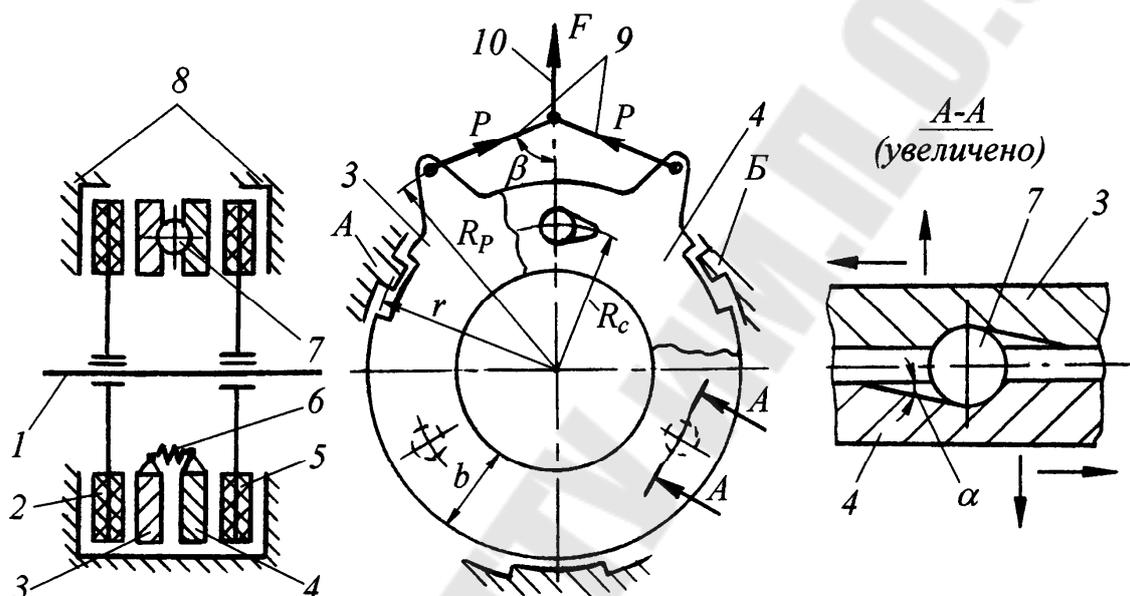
Схема закрытого дискового тормоза с сервоусилением.
